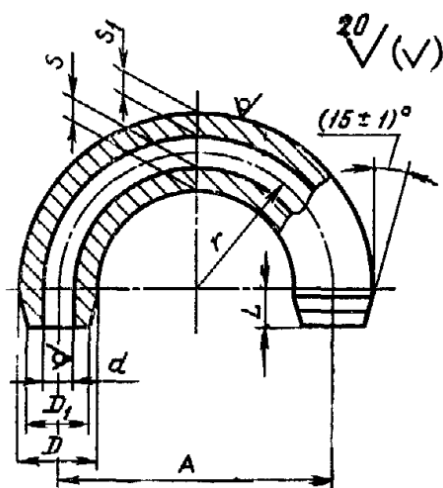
Эскиз и общий вид отвода «колено двойное» [2]
